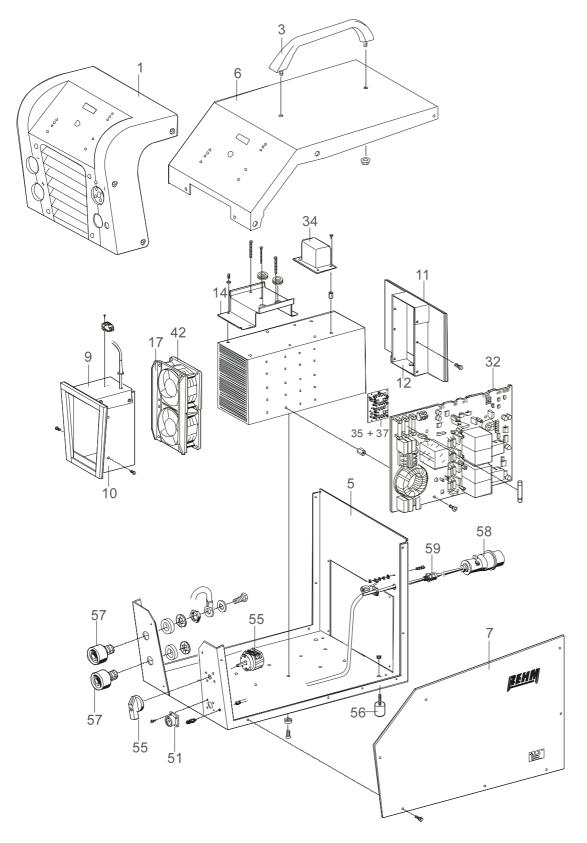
Explosionszeichnung BOOSTER.PRO 250 / 320 (rechts)
